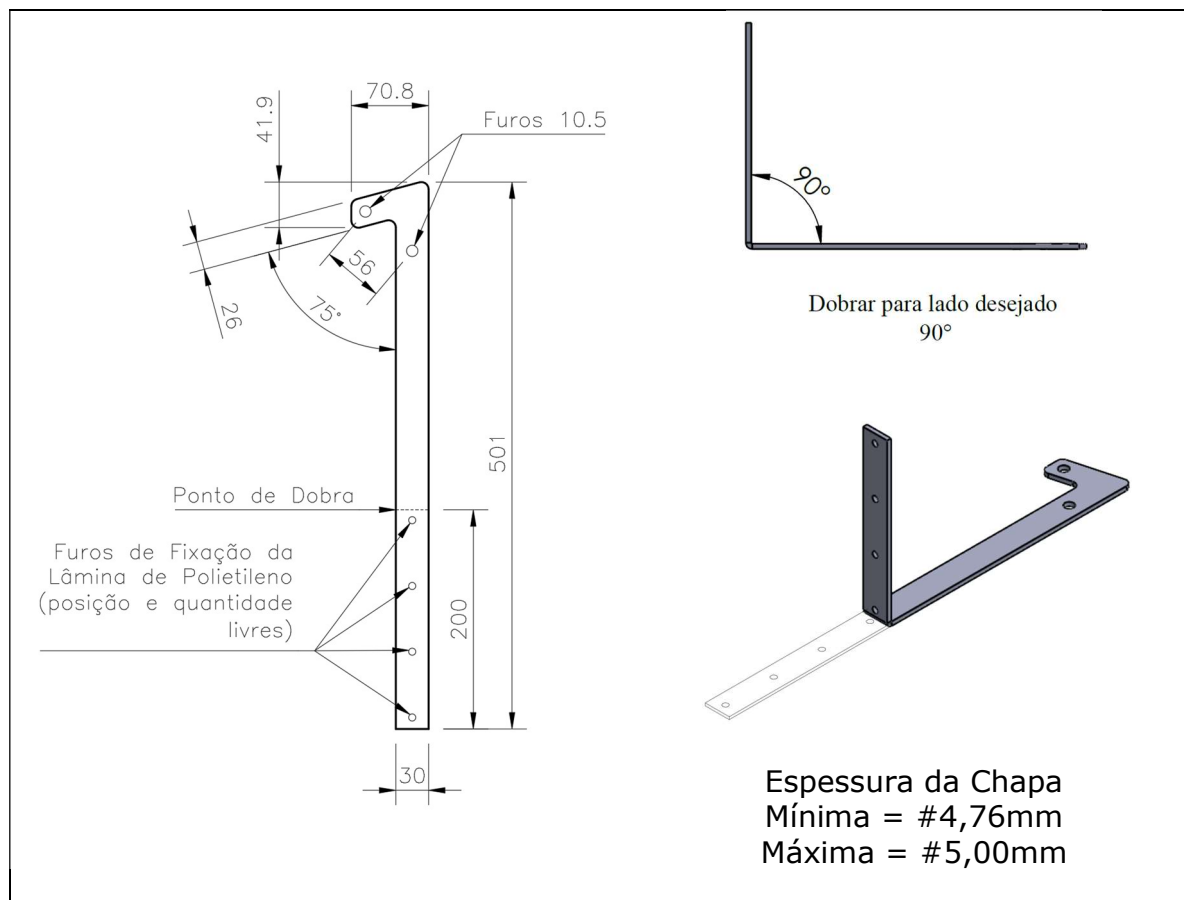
detalhamento do suporte do para-barros dianteiro
